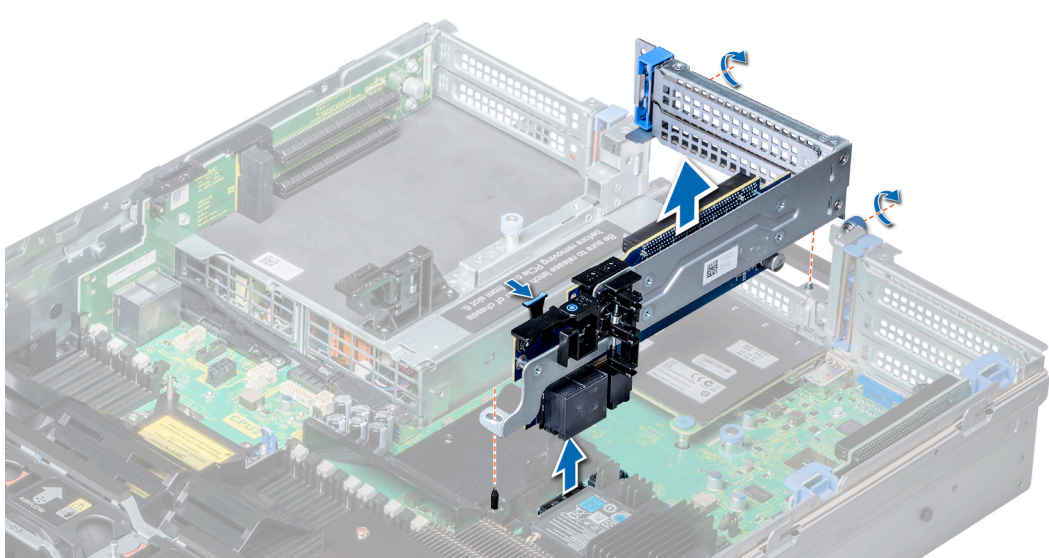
Retrait des cartes de montage pour carte d'extension 2A
